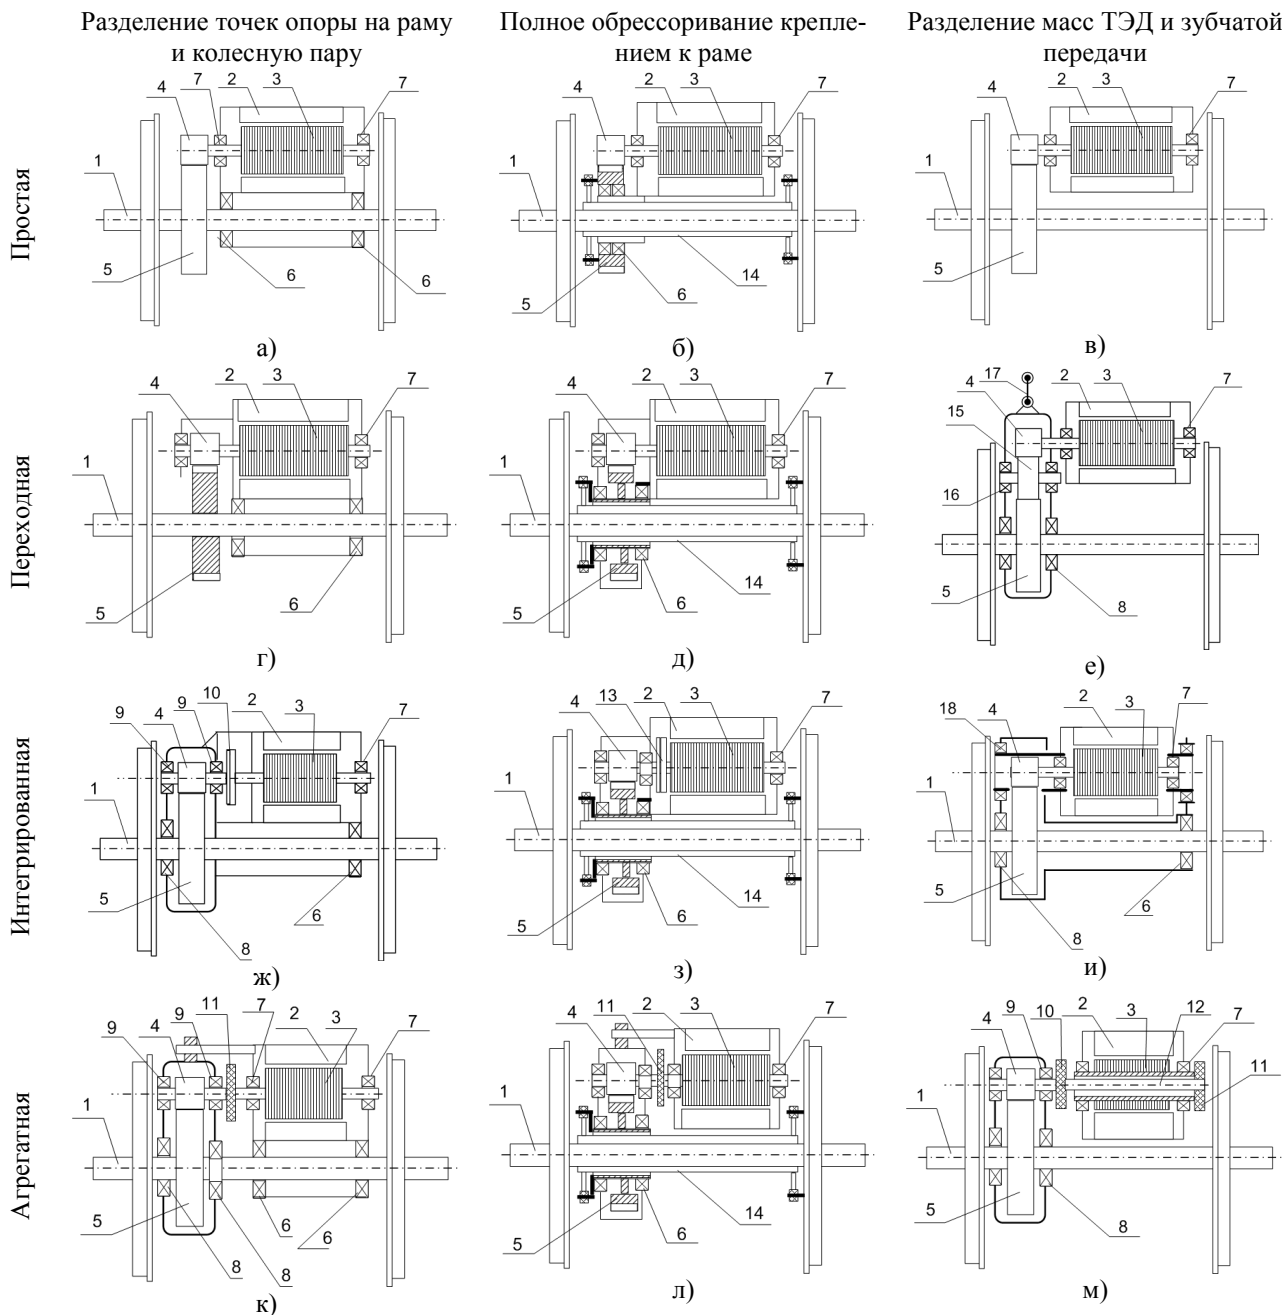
Табличная классификация групп конструктивных решений для редукторных приводов: 1 – колесная пара; 2 – статор ТЭД; 3 – ротор ТЭД; 4 – малое зубчатое колесо; 5 – большое зубчатое колесо; 6 – моторно-осевой подшипник; 7 – подшипник ротора ТЭД; 8 – осевой подшипник редуктора; 9 – подшипник оси малого зубчатого колеса; 10 – дисковая муфта; 11 – упруго-компенсирующая муфта; 12 – торсионный вал; 13 – мембранная муфта; 14 – полый вал; 15 – промежуточное зубчатое колесо; 16 – подшипник промежуточного зубчатого колеса; 17 – тяга; 18 – подшипник опоры на вал ТЭД
